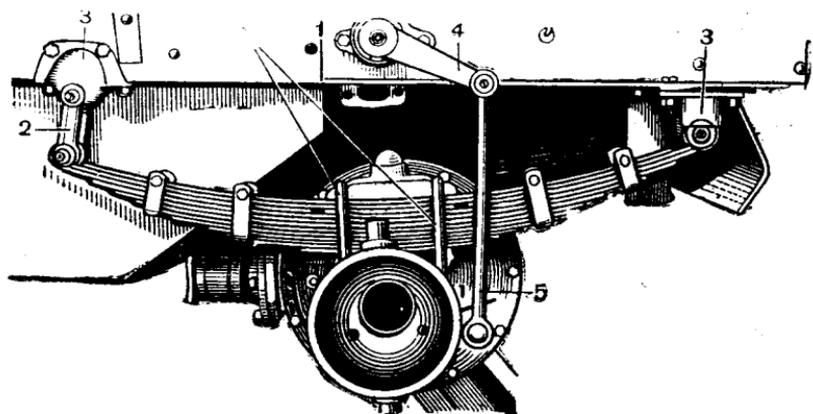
Крепление рессоры и амортизатора к раме самоходного орудия:
